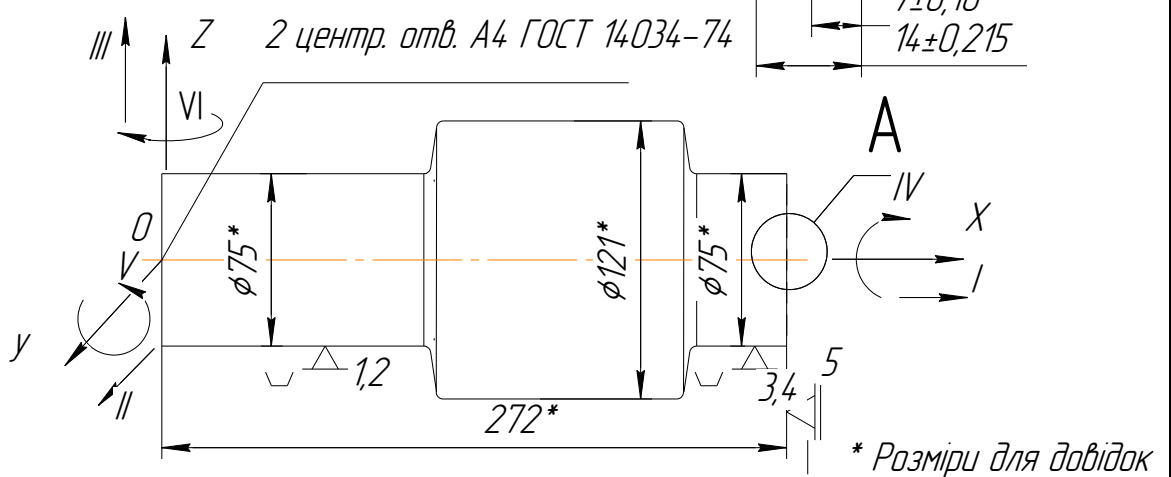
Альтернативна схема базування на фрезерно-центрувальній операції
